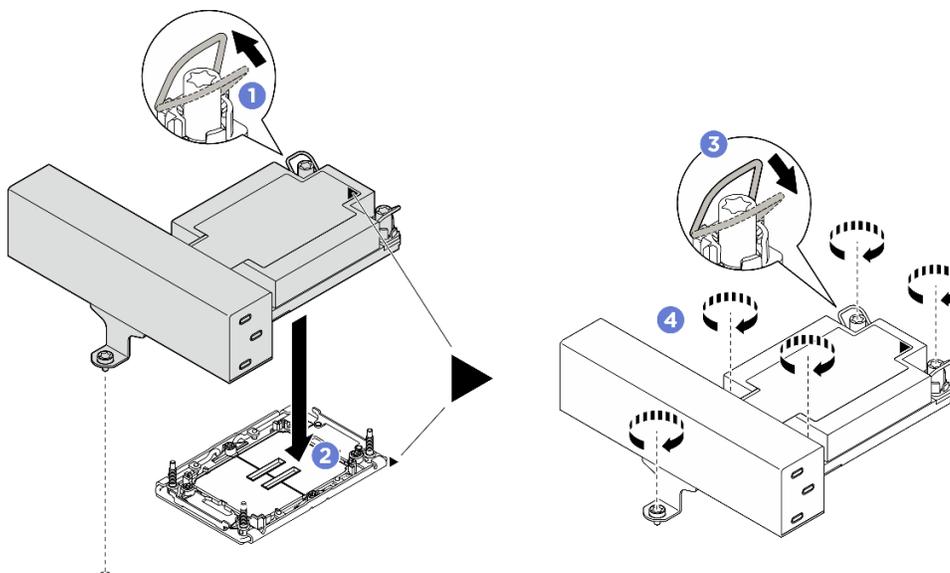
Installation d'un module de processeur-dissipateur thermique de performances 1U en forme de T
